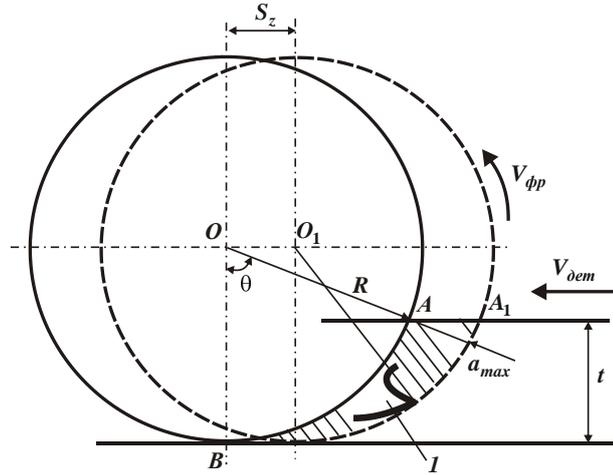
Расчетная схема параметров процесса фрезерования цилиндрической фрезой: 1 – зуб фрезы.
